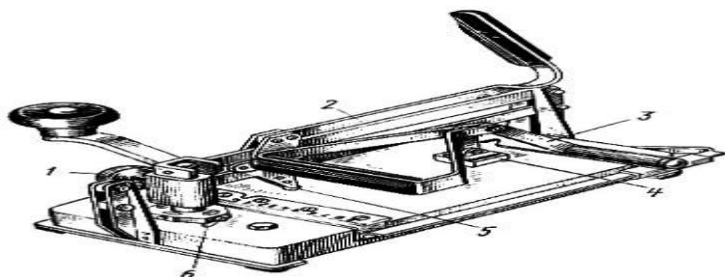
Плиткорез с головкой для сверления отверстий в глазурованной плитке: 1 - каретка, 2, 3 - рычаги, 4 - прижим, 5 - ролик, 6 - резец
